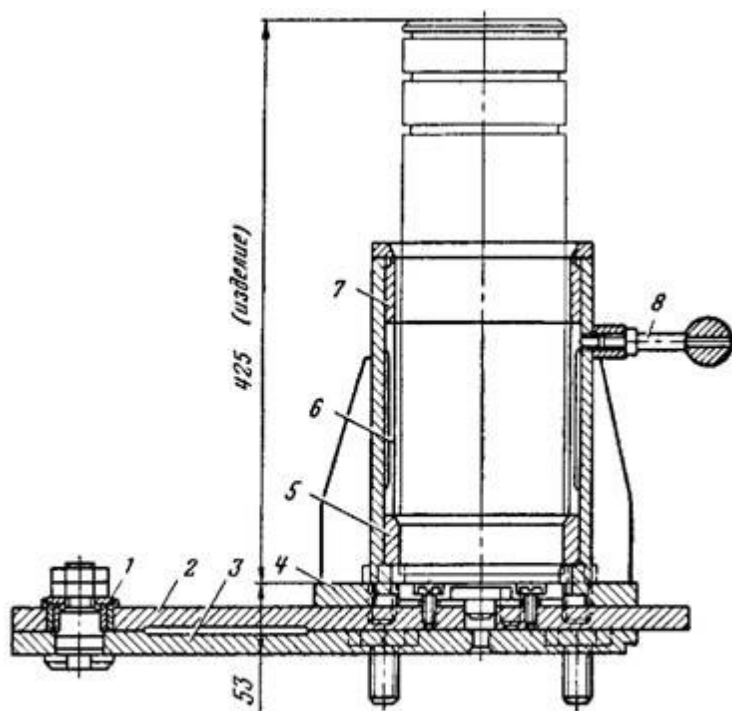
Приспособление для сборки телескопического подъемника
